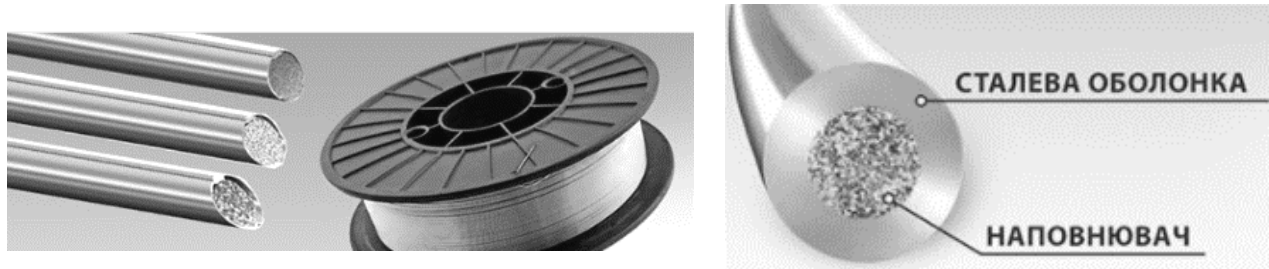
Порошковий дріт для зварювання та наплавлення
